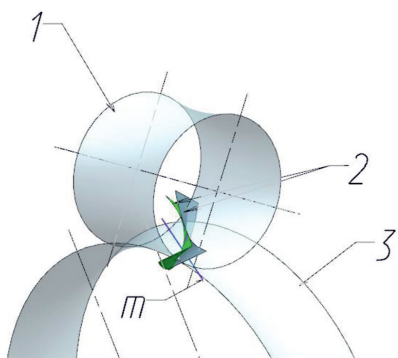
Совмещенные поверхности зубьев, участвующих в зацеплении. 1 – делительный гиперболический конус ведущего колеса; 2 – сопряженные боковые поверхности зубьев; 3 – делительный гиперболический конус ведомого колеса
